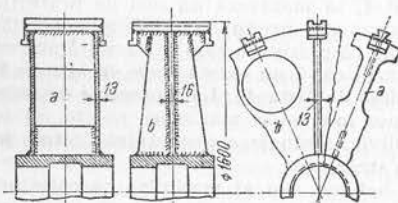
Butuc de rotor sudat: a — cu două discuri frontale; b — cu un singur disc.
